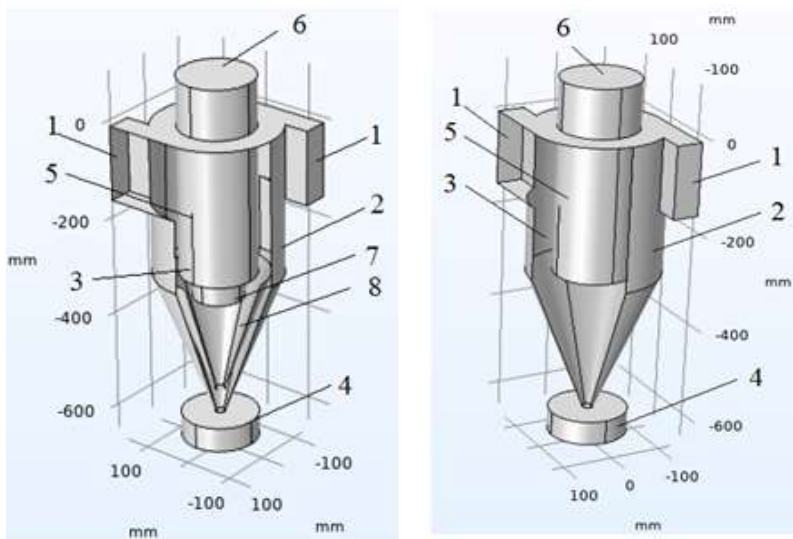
Модифицированный центробежный пылеуловитель. 1- вход в спиральный воздухозаборник, 2- цилиндрический корпус пылеуловителя, 3- конусный корпус пылеуловителя, 4-бункер, 5- труба для отвода очищенного воздуха, 6-выход очищенного воздуха, 7-стабилизатор потока, 8-внутренний конус.
